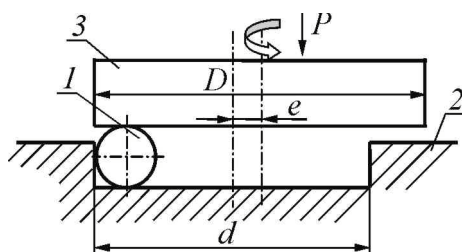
Схема накатывания сферической заготовки плоскими поверхностями
